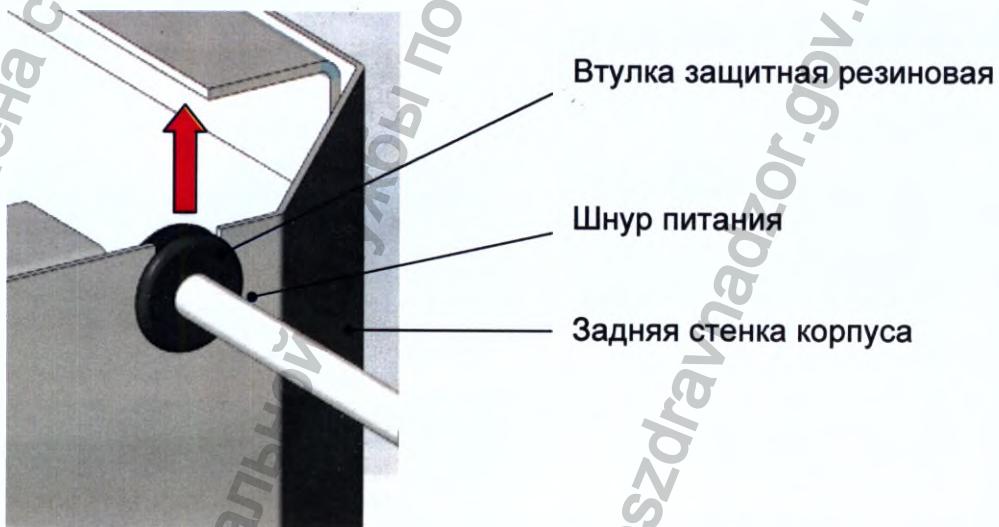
Выемка втулки защитной резиновой со шнуром питания.
